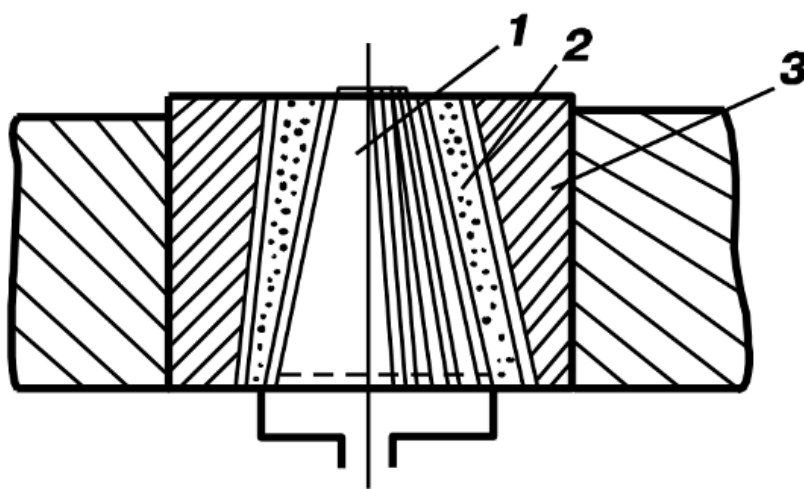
Установка пористої вставки в днище ковша:
